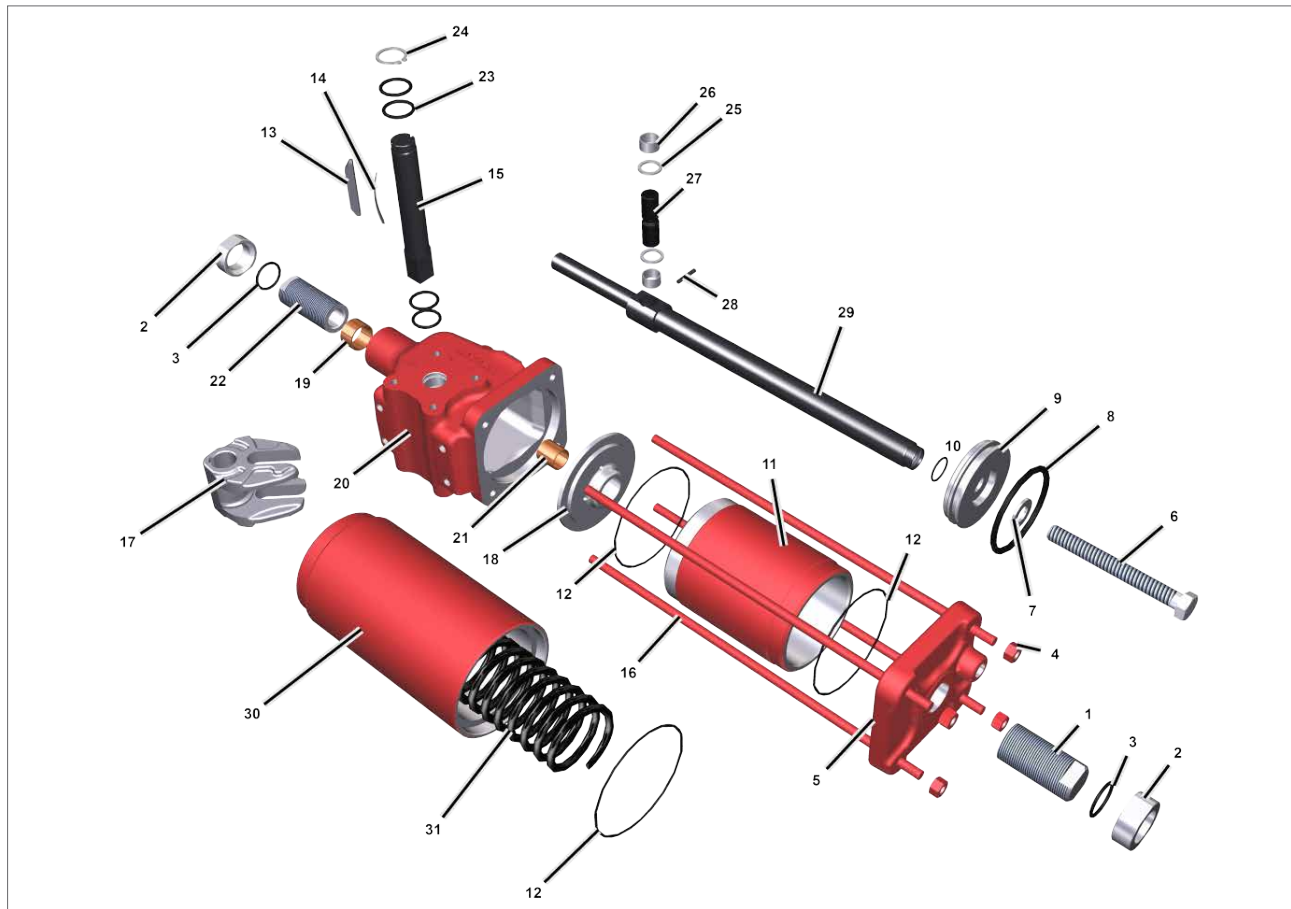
Привод одностороннего действия (размер 055-065) с переходной пластиной
